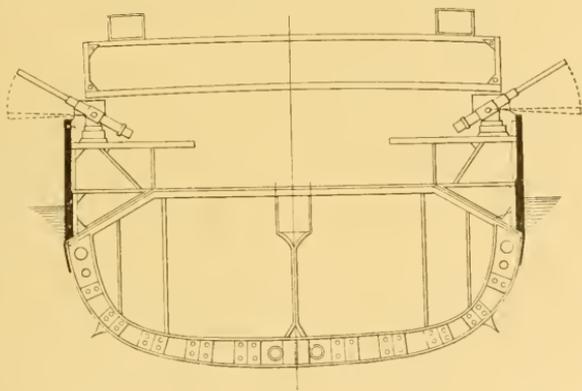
Coupe transversale d'un cuirassé de construction moderne.
